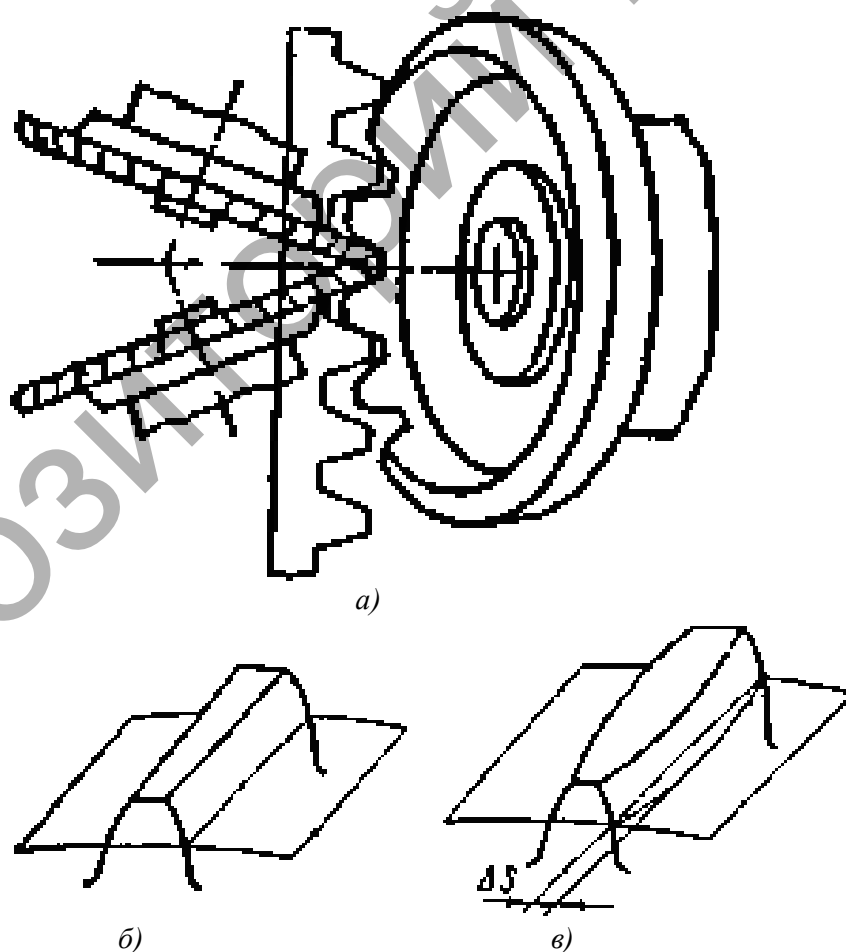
Схема работы станка для нарезания конических зубчатых колес дисковыми фрезами по методу обката и виды получаемых зубьев
